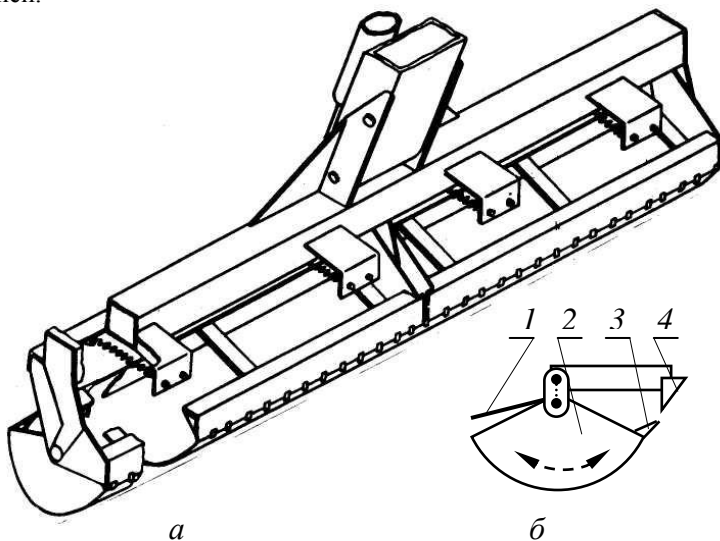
Уширенный поворотный ковш с неподвижной заслонкой и противорезающей кромкой: а – общий вид; б – схема работы.
